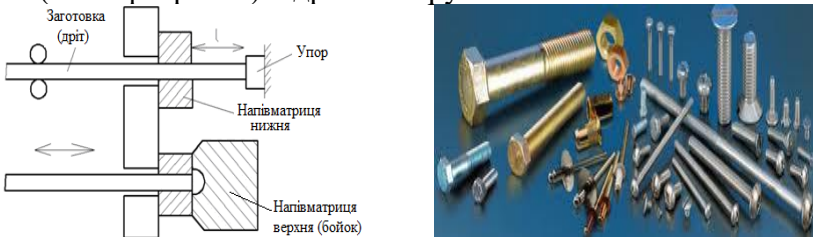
Схема штампування висадженням (а) та отримувані заготовки (б)
